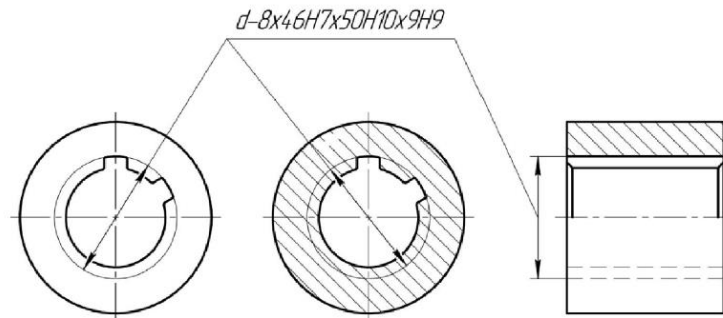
Зображення на кресленнях шліцьової втулки
